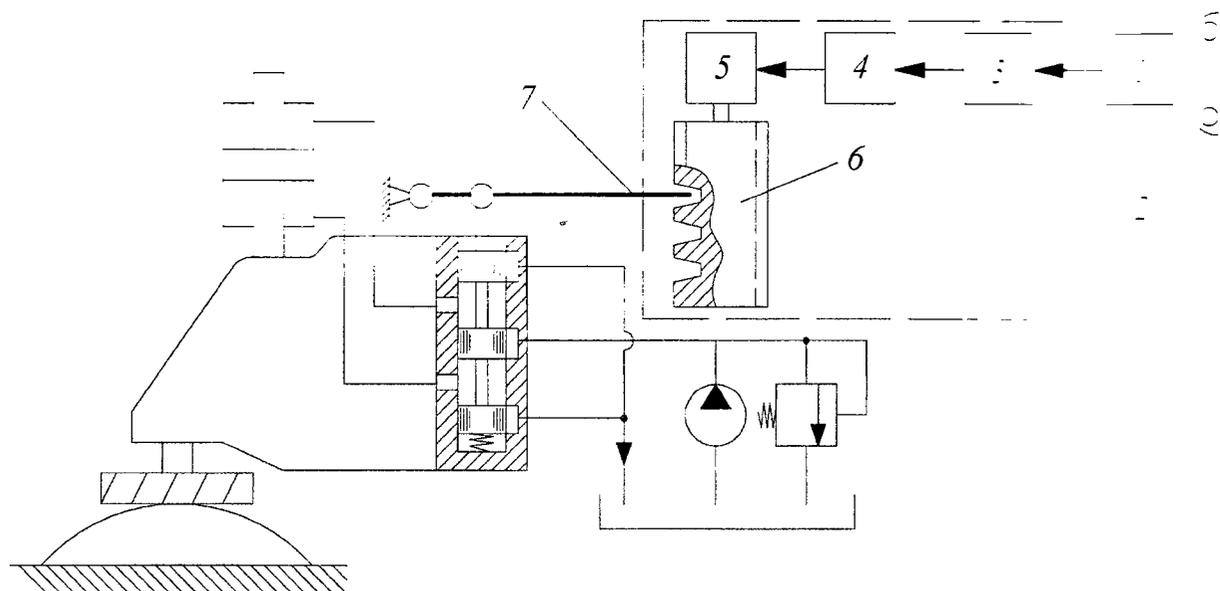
Гидропривод копировально-фрезерного станка с ЧПУ
